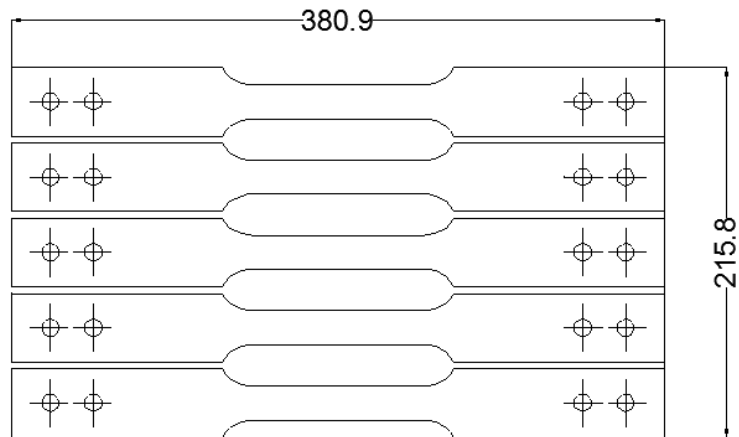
Disposición de las probetas para su extracción de la plancha fundida
